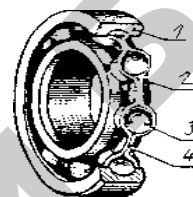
Шариковый радиальный однорядный подшипник
